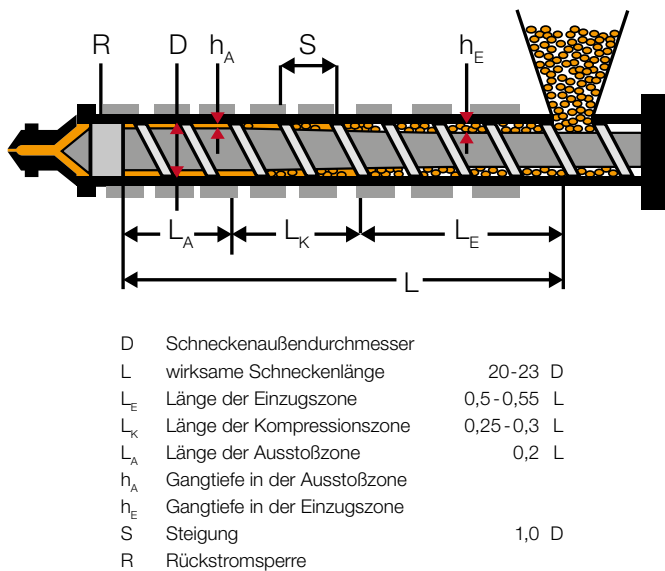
Schneckenengeometrie; Begriffe und Maße von Dreizonenschnecken für Spritzgießmaschinen
